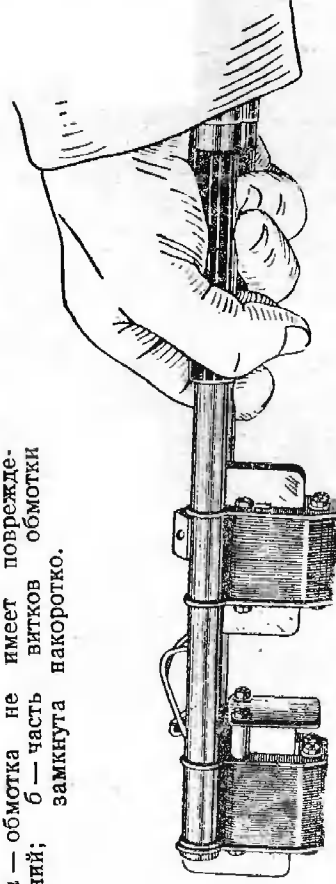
Приспособление с двумя электромагнитами для обнаружения пазов с короткозамкнутыми витками.
